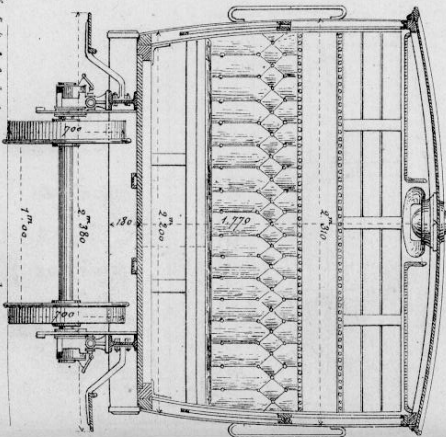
Elevation, Coupe transversale à 0^m03 p^r 1^{er} Mètre.
